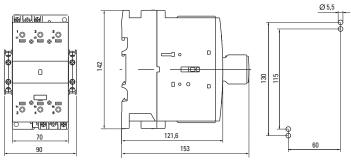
Габаритные и установочные размеры контакторов КМЗ 80А, КМЗ 90А, КМЗ 100А
